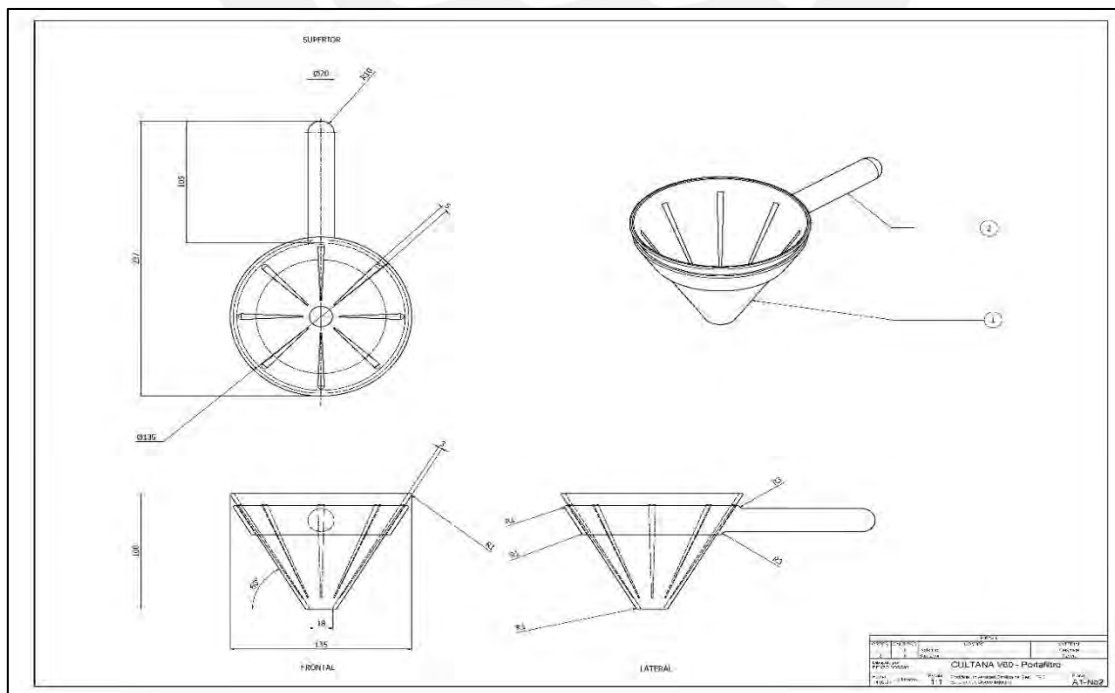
Plano 1.1 - vistas de sección de la parte soporte
